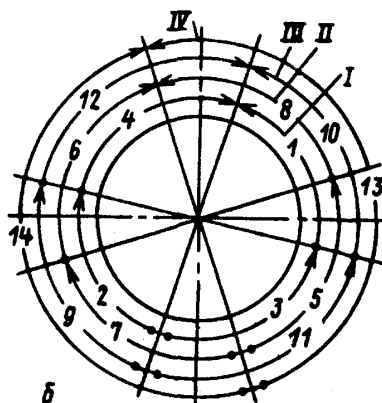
Схема наложения слоёв при сварке вертикального неповоротного стыка
